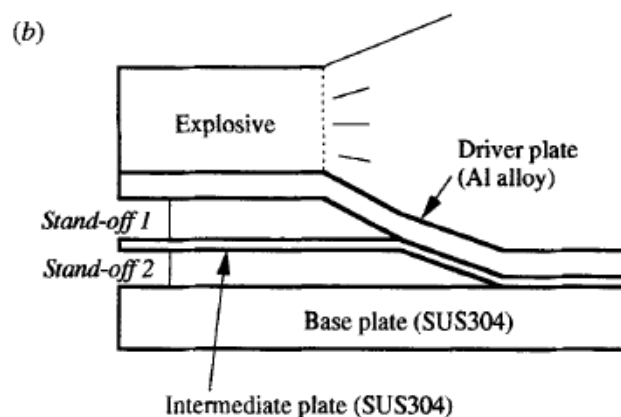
Técnica de soldadura por explosão utilizando uma placa intermédia (Hokamoto, et al., 1993).
